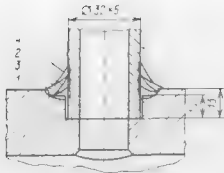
Способ приварки трубы змеевика к коллектору
